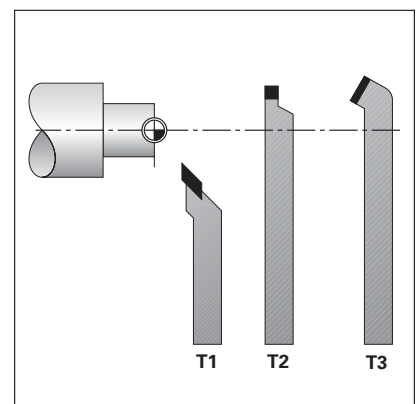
Die dargestellten Werkzeuge haben unterschiedliche Werkzeug-Daten
